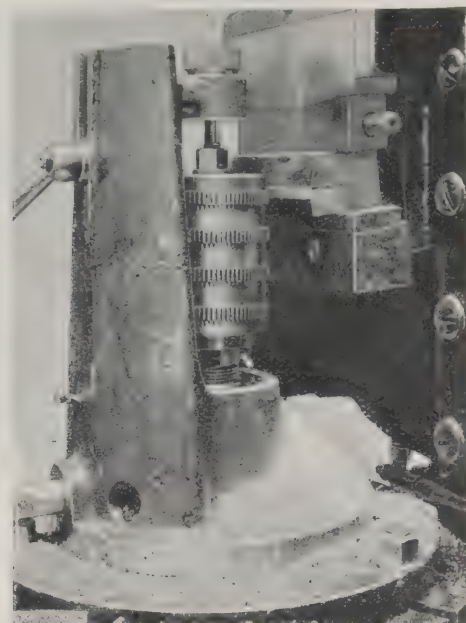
Zahnrad-Stoßmaschine von Maag mit langem Kamm.
